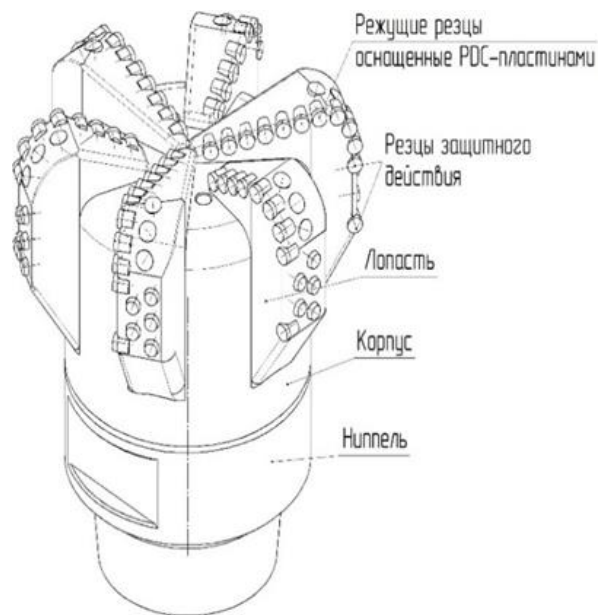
Конструктивные особенности бурового долота с PDC-резцами
